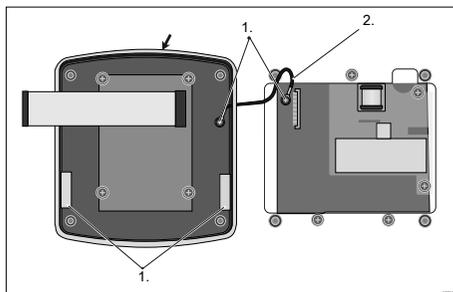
En cas de montage encastré : Monter le joint profilé sur la partie supérieure du boîtier du régulateur
